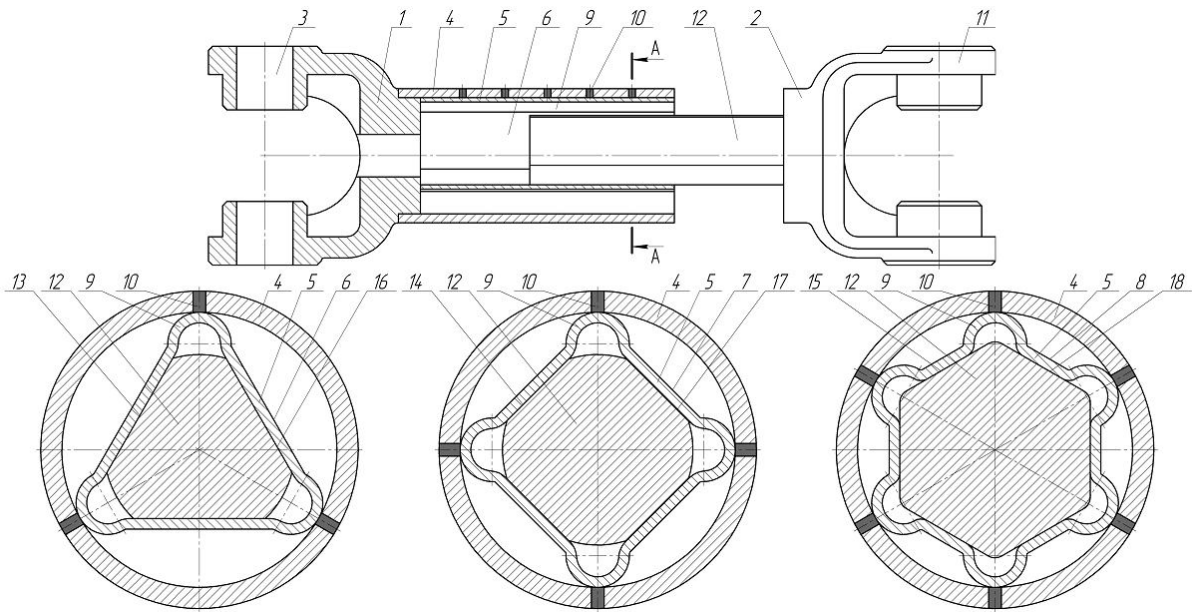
Конструктивна схема нового вала карданної передачі з різними перетинами
